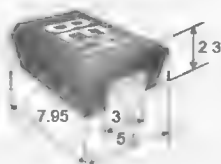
Внешний вид и размеры корпуса DO-214AB
